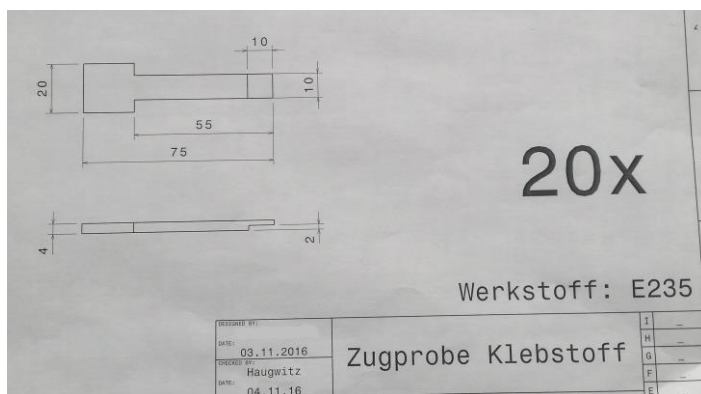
Ausschnitt aus der Werkstattzeichnung für die Zugproben
